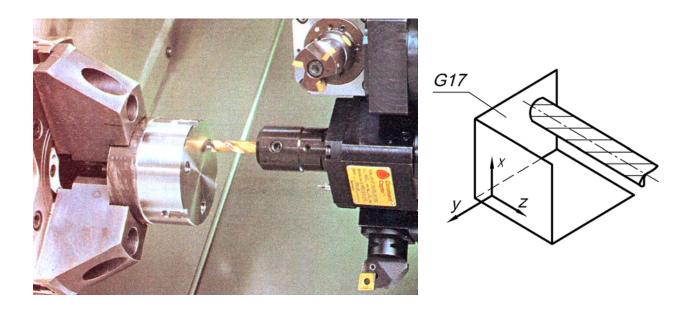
Фрезерный инструмент в плане обработки X-Y на многофункциональном центре: рабочая зона станка и схема плана фрезерной обработки детали
